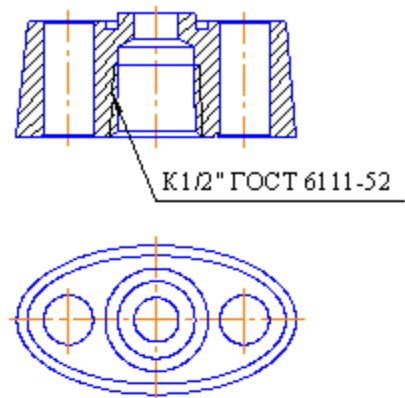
КМЧ: овальный фланец с резьбой K1/2"
